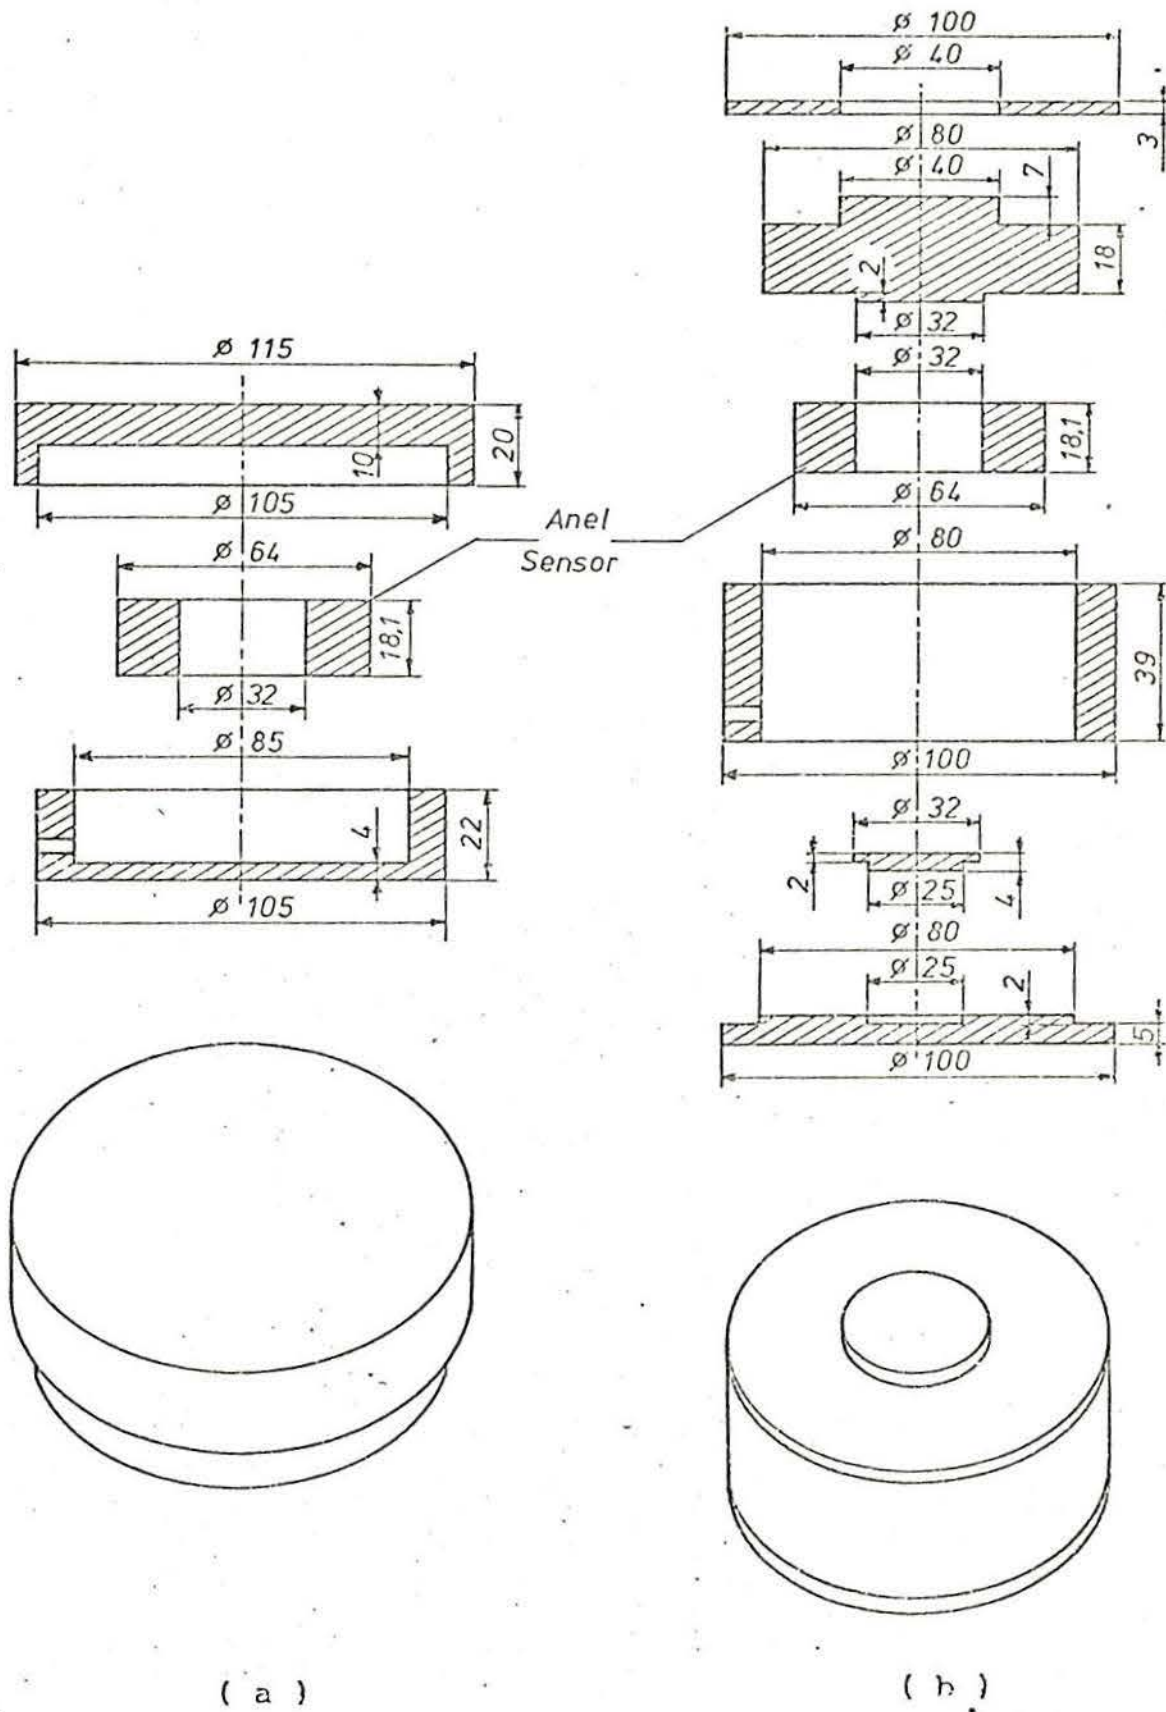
a) - Sensor ou célula de carga construído para a laminação 1.
